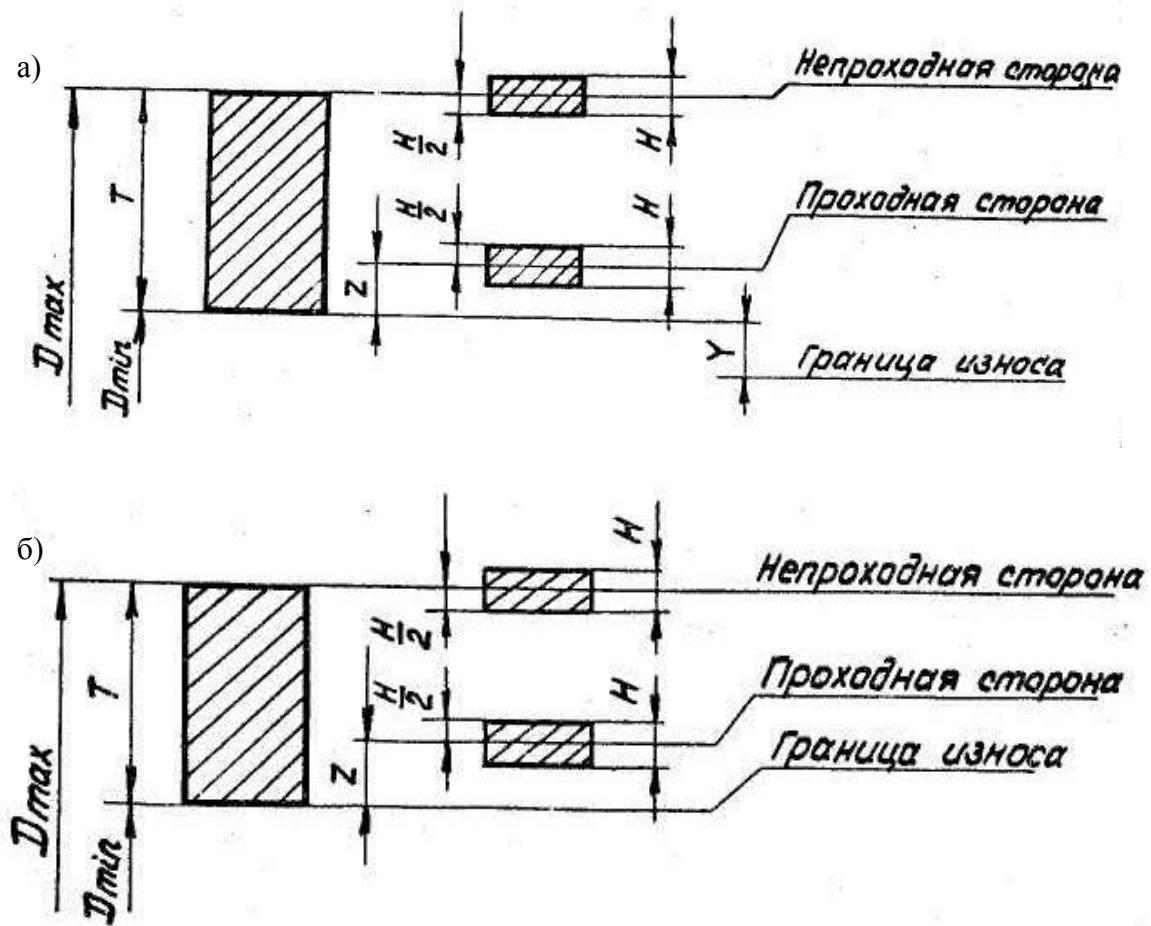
Схемы расположения полей допусков калибров-пробок для номинальных размеров до 180 мм
